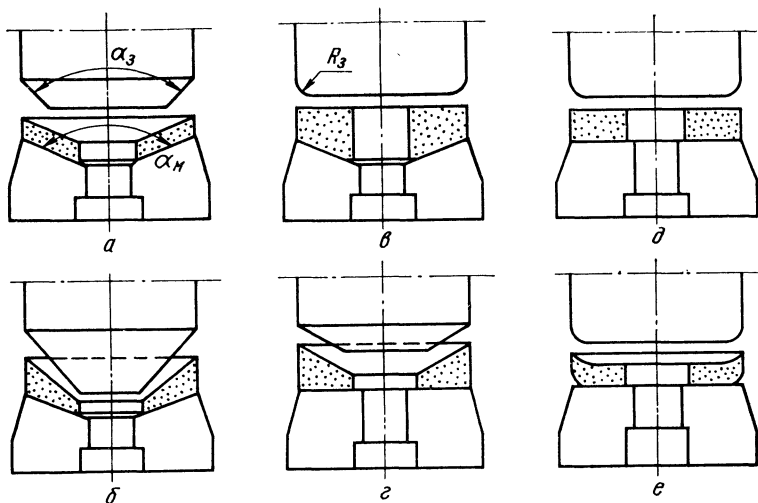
Формы шайб из стеклопорошка при различном профиле матрицы и переднего конца заготовки [164]
